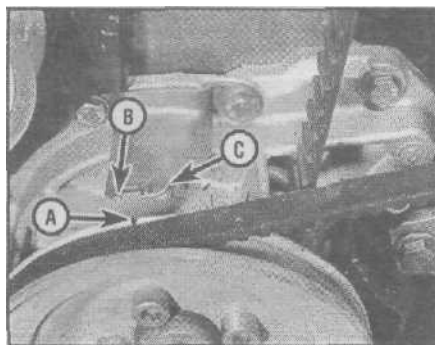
, а. Метка шкива коленчатого вала (А), установочная метка (В) и метка верхней мертвой точки [С] (крышка ремня снята) - двигатель 1,3 литра
